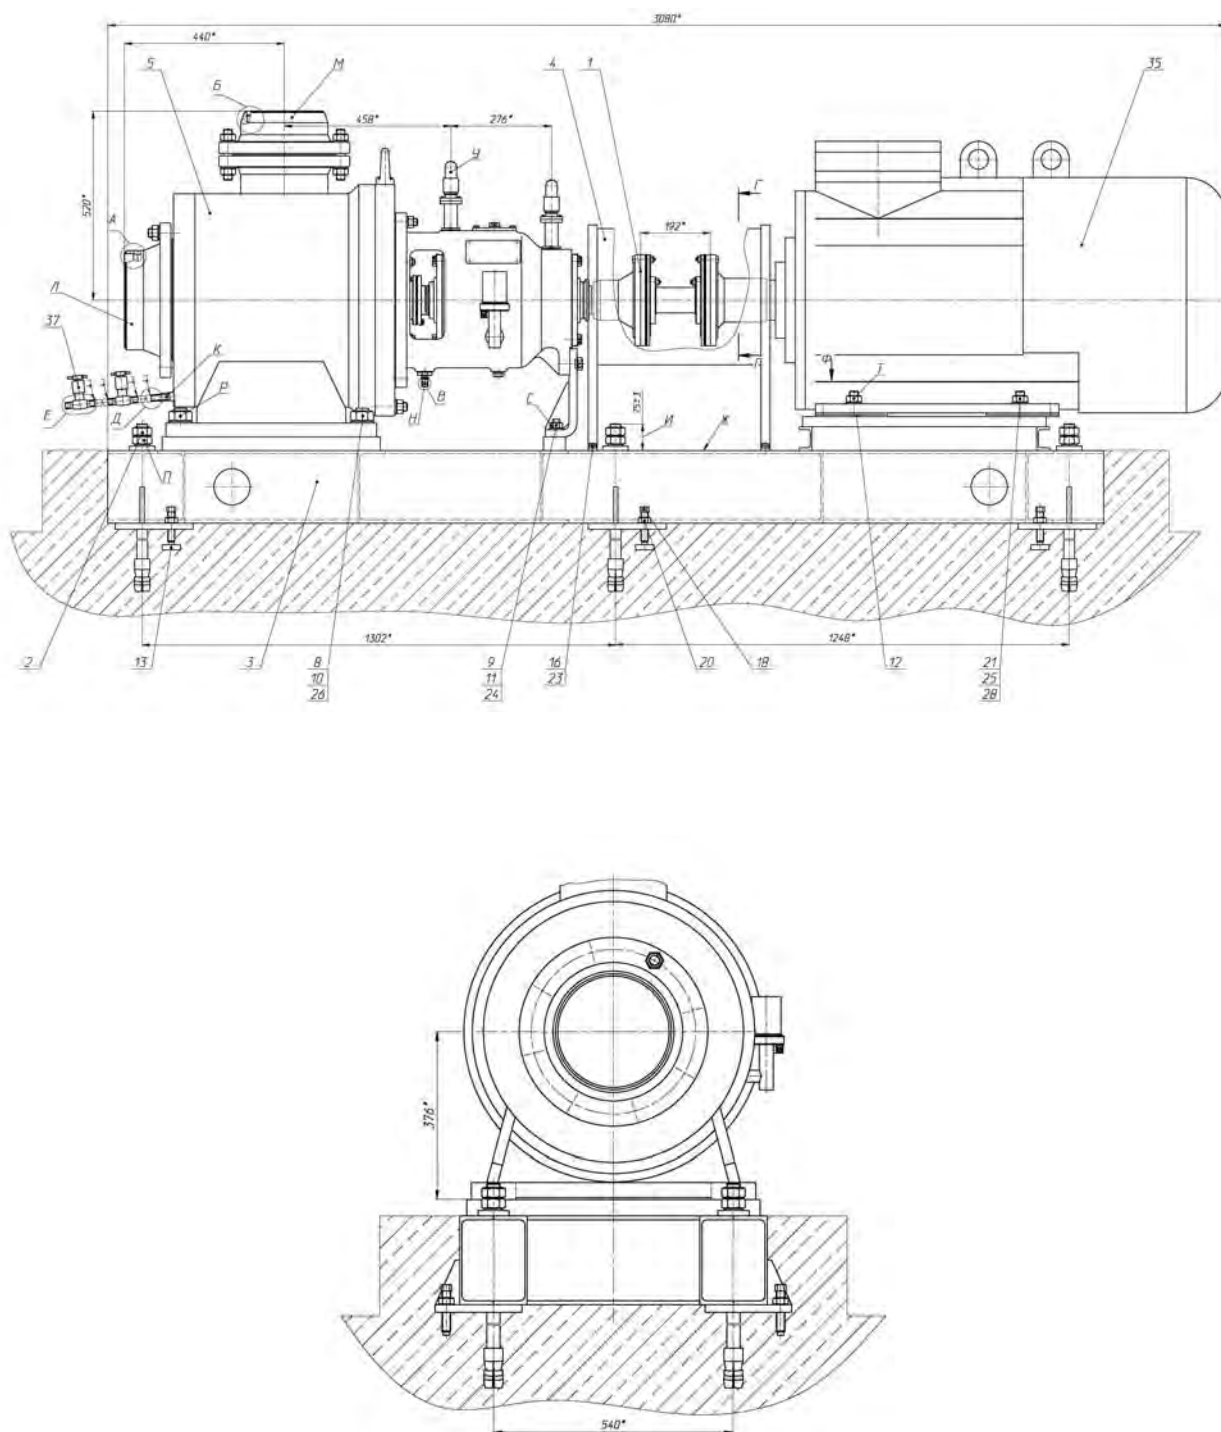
Габаритный чертеж спринклерного насоса
